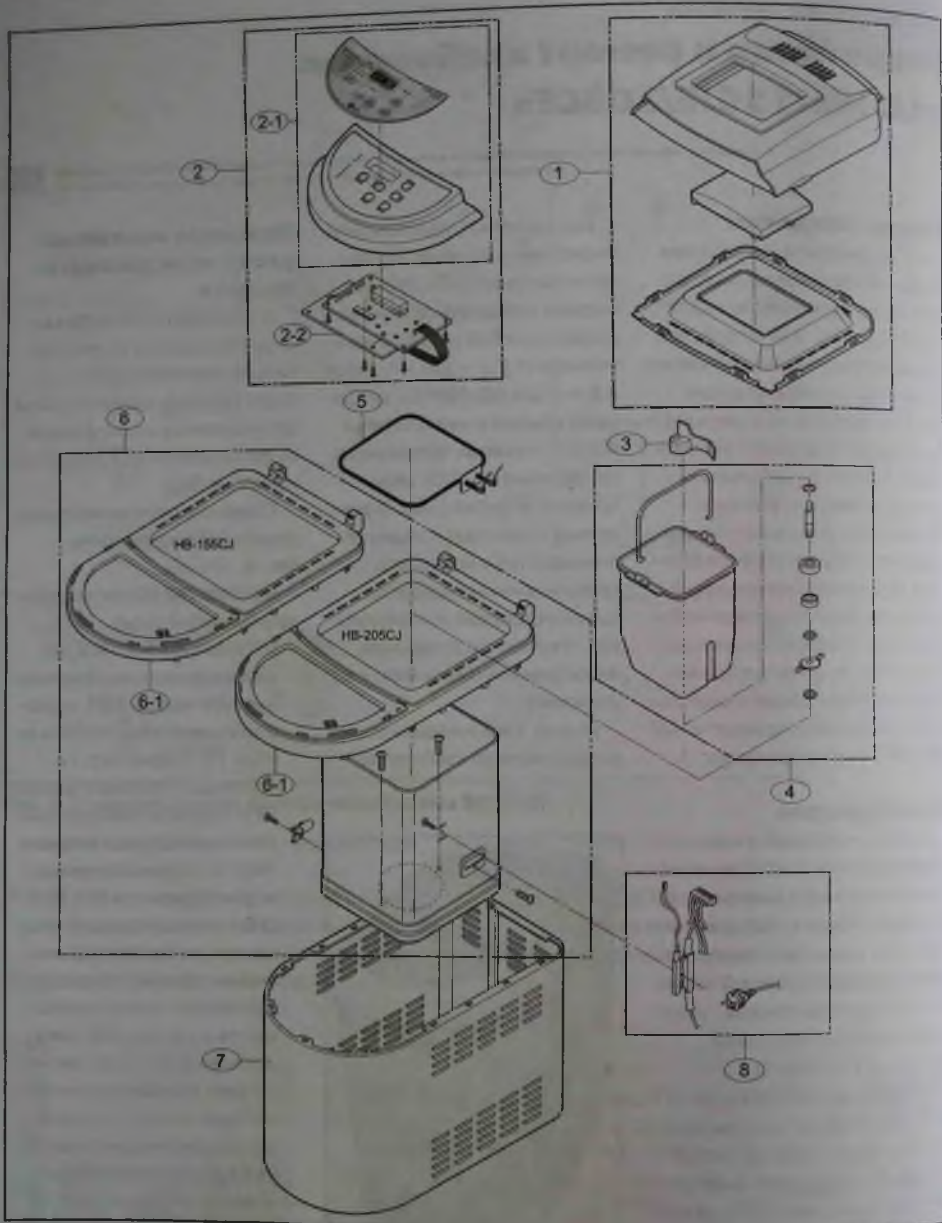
Сборочный чертеж хлебопечек (1), где: 1 — верхняя крышка, 2 — ПУ и ЭМ (2-1 — крышка ПУ; 2-2 — платы ПУ и ЭМ), 3 — лопатка, 4 — контейнер с валом лопатки, 5 — ТЭН, 6 — крышка с внутренним кожухом, 7 — внешний кожух, 8 — проводные соединители в сборе с датчиком температуры
